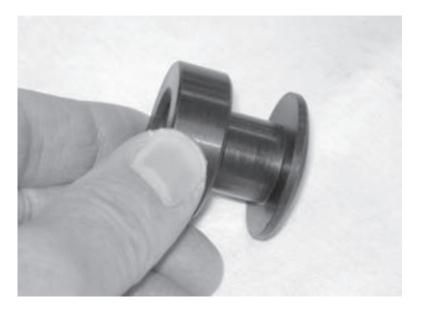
Schrauben Sie die Spannfüße in das Spanngehäuse.
